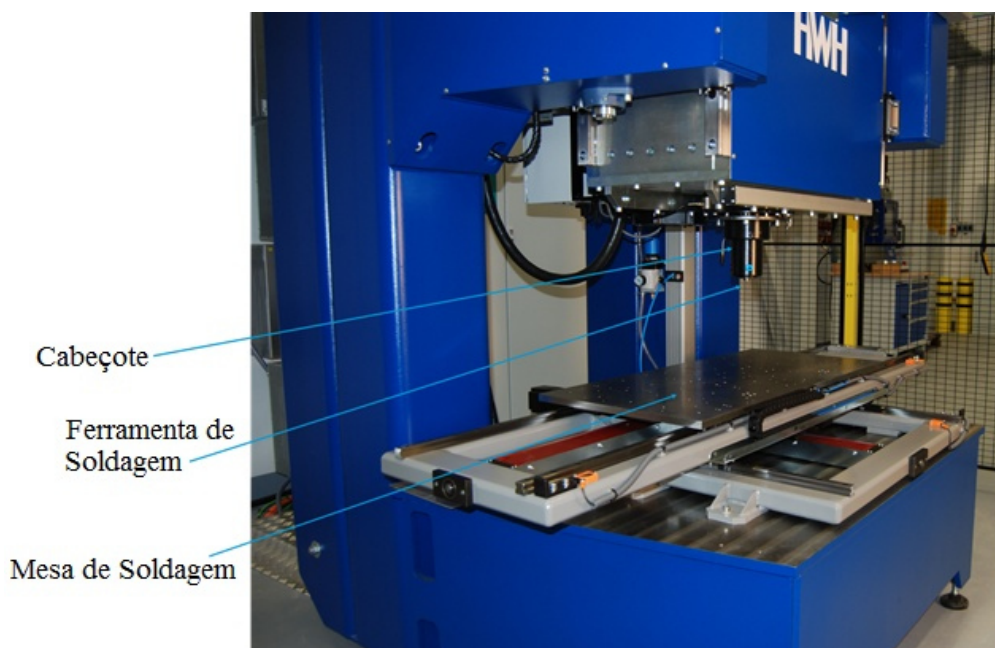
Equipamento de soldagem FSpW Harms & Wende RPS 200.
